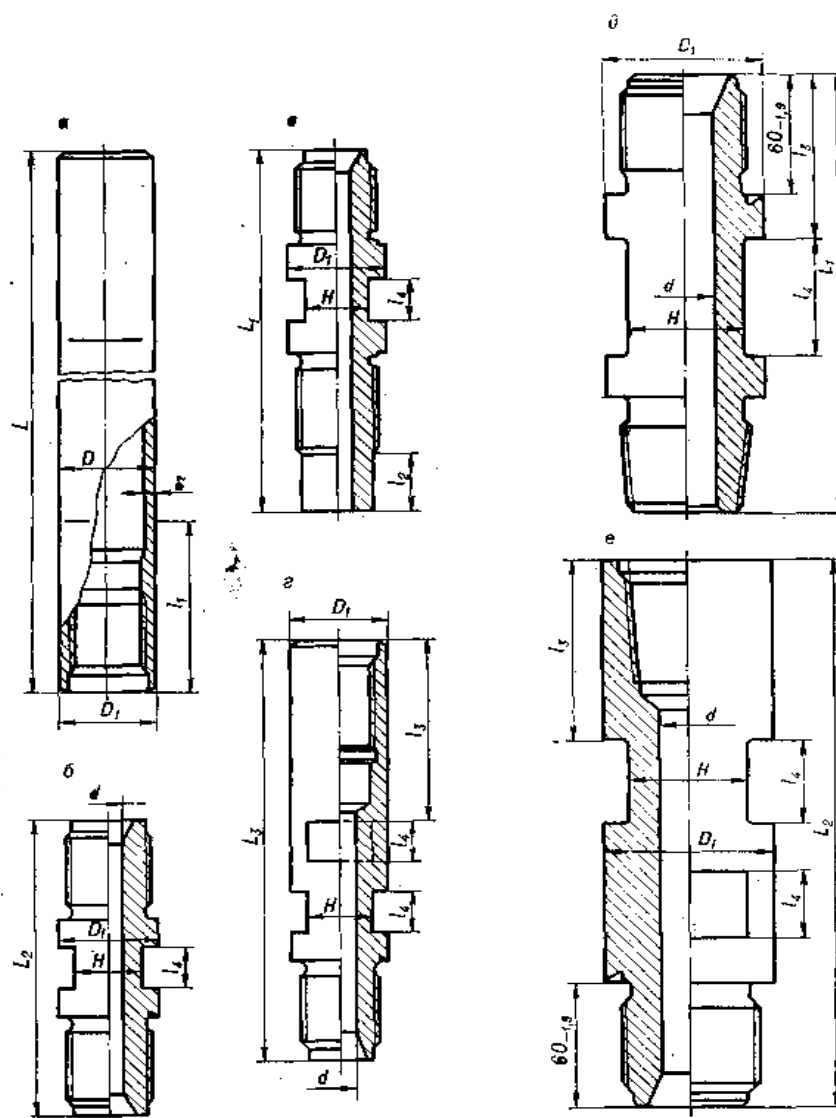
Стальные буровые трубы ниппельного соединения: а – буровая труба; б – ниппель трубный соединительный (типа В); в – ниппель типа А диаметром; г – полуниппель (ниппель типа В); д – ниппель типа А; е – полуниппель
